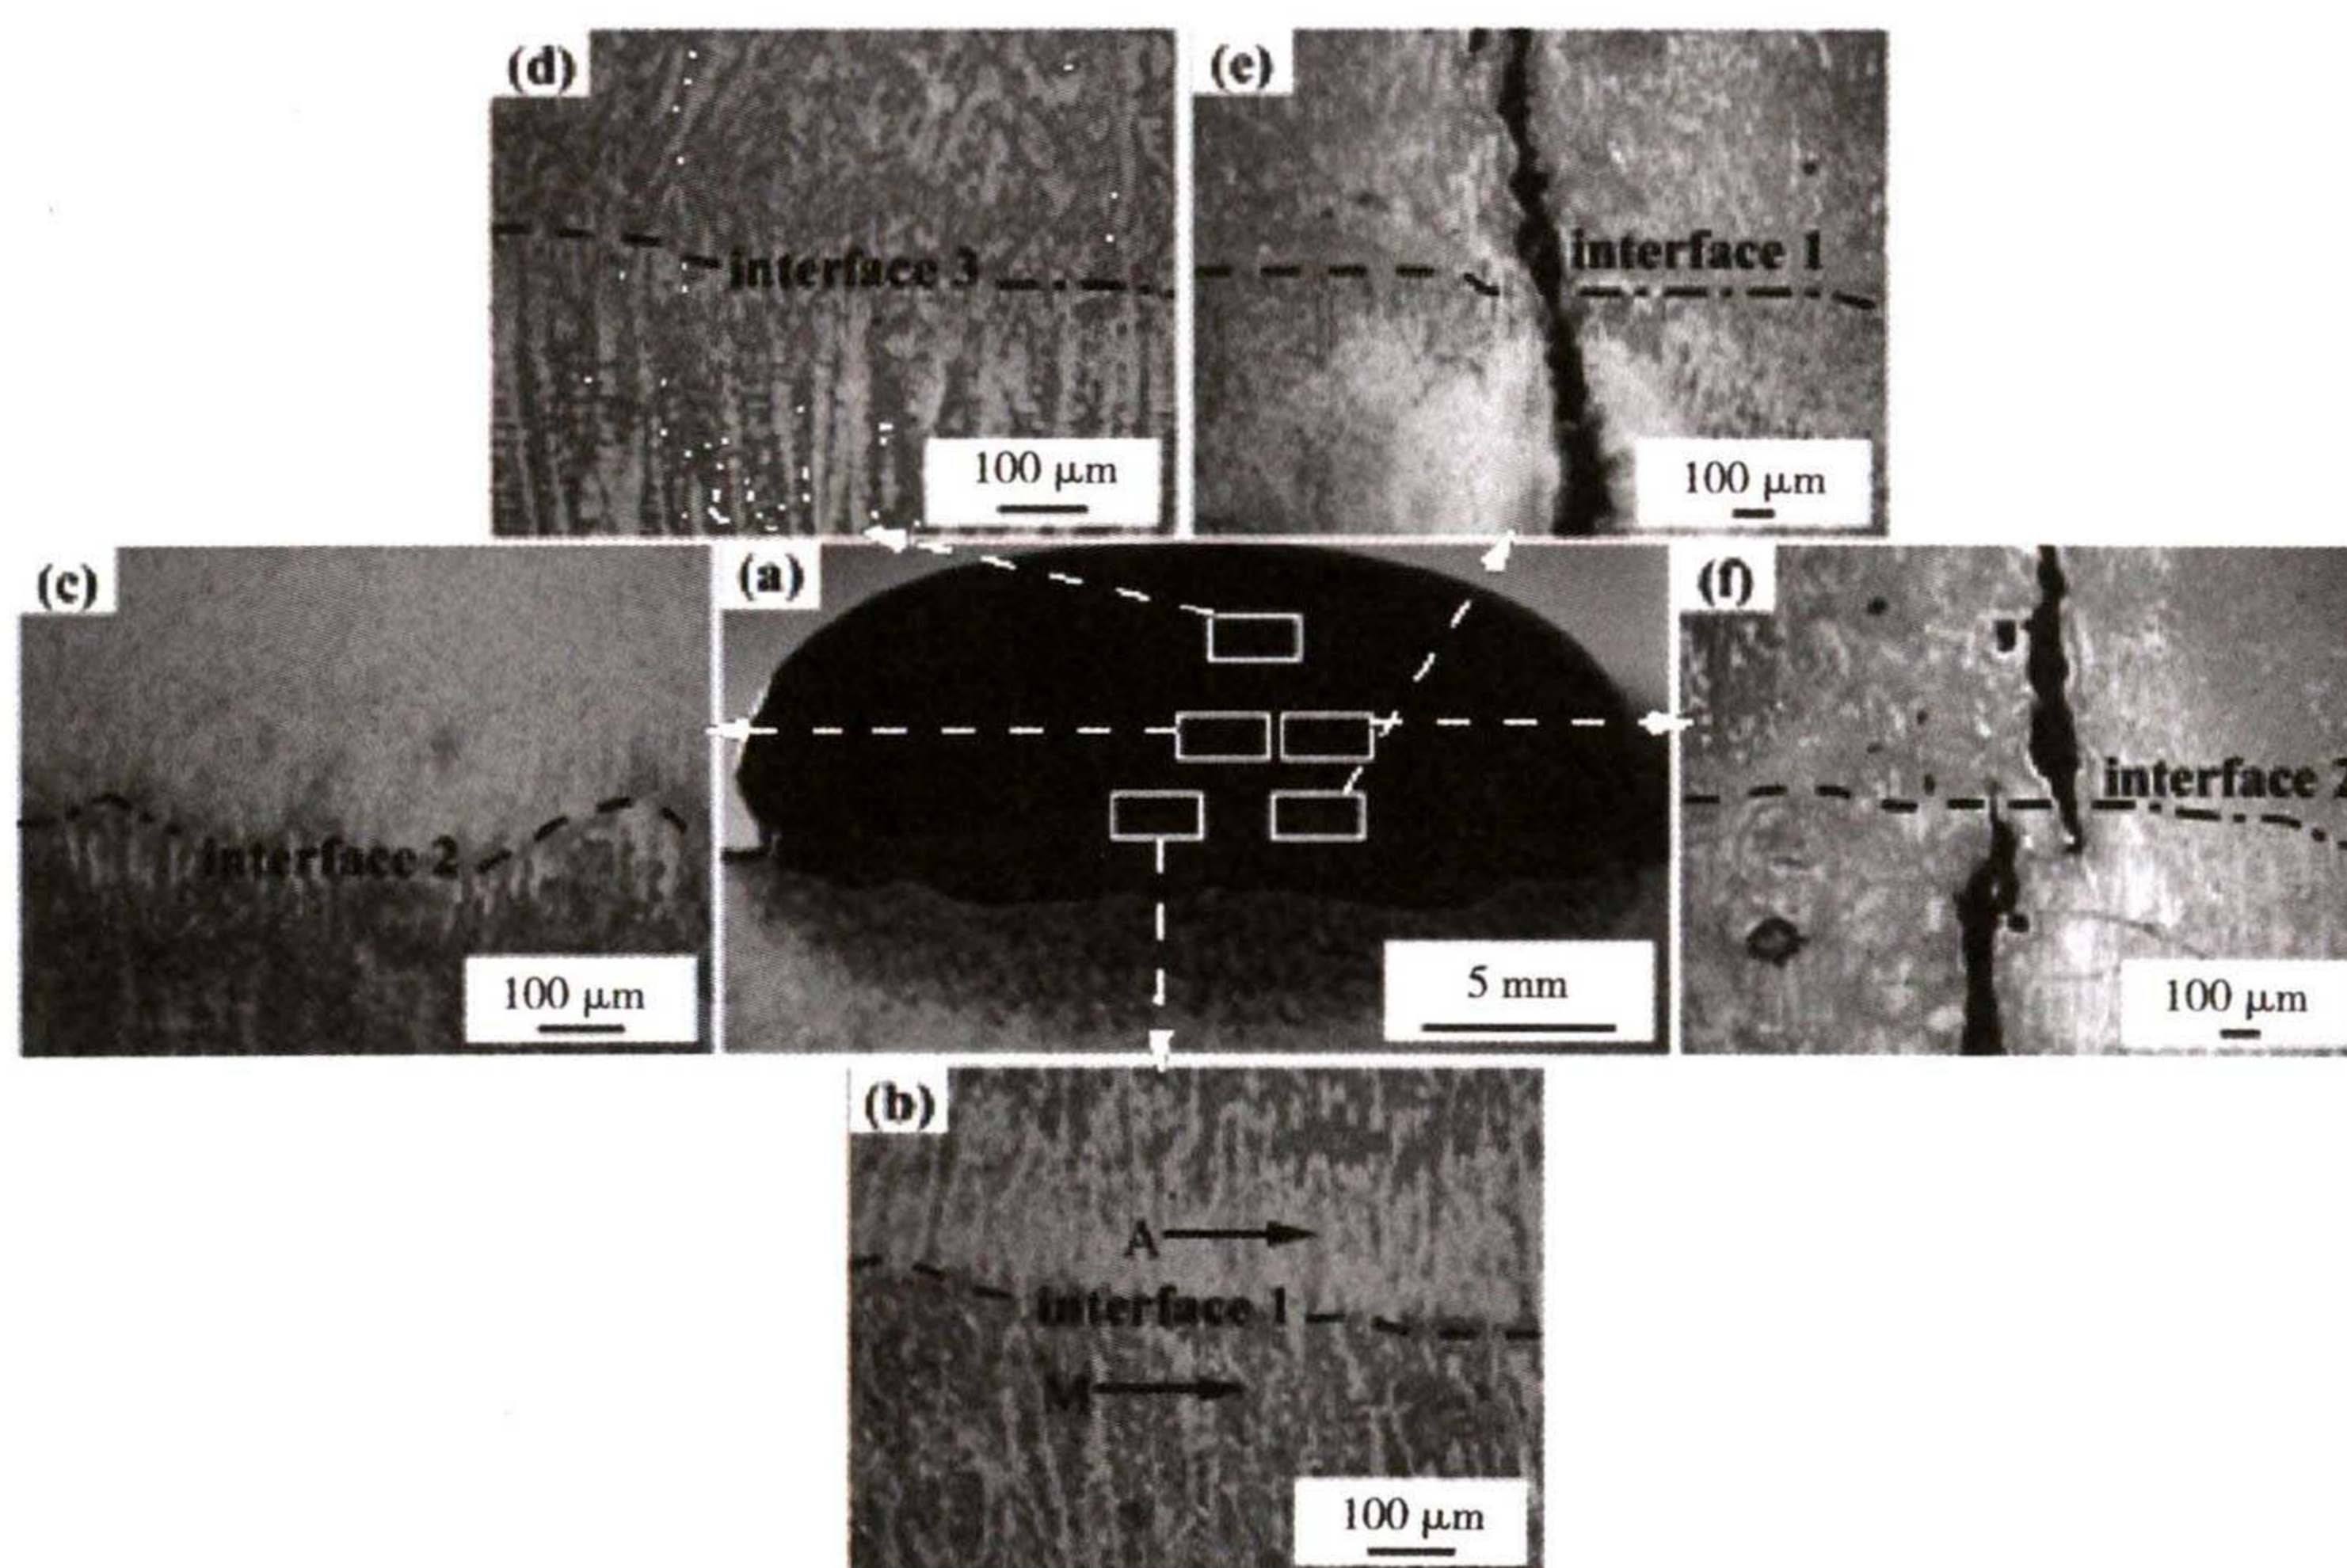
焊接电流 130 A 条件下,焊接四层时试样的宏观形貌、显微组织形貌以及裂纹形貌
